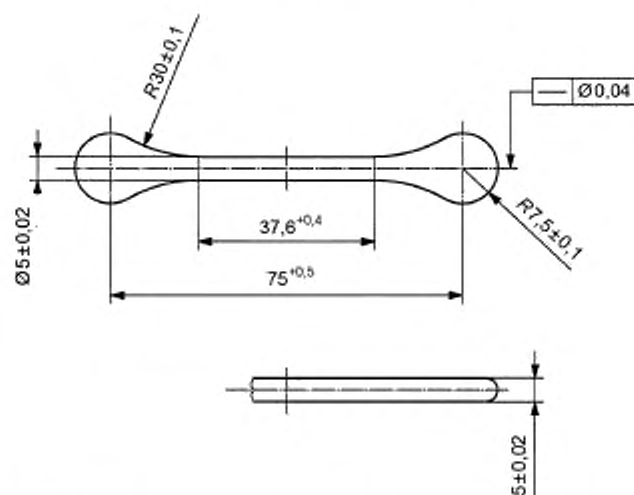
Эскиз полости пресс-формы для изготовления образцов-свидетелей для испытаний на растяжение типа В
